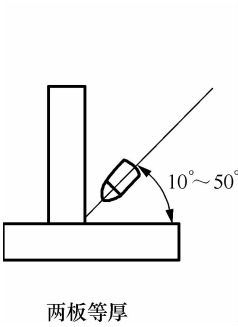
40 T 形接头焊接时焊丝的角度
